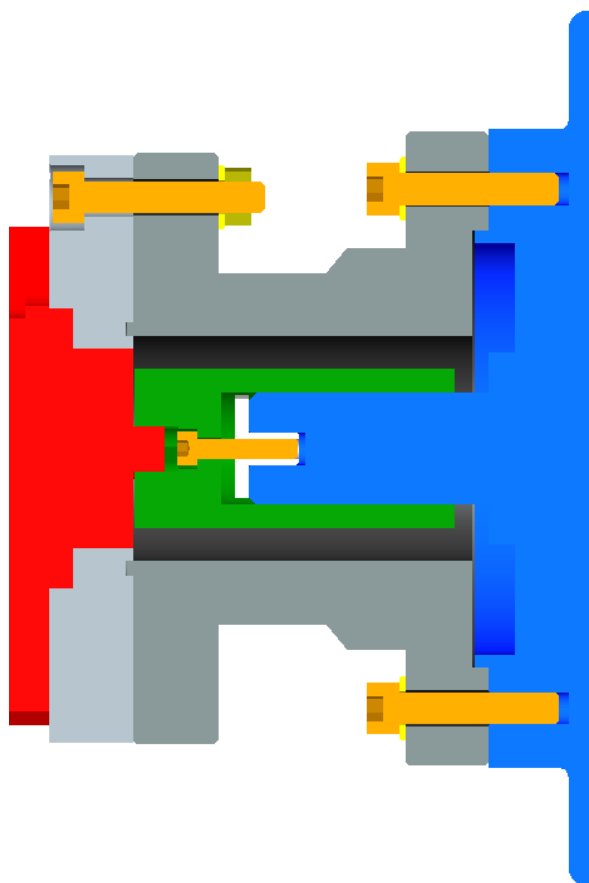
Spojení spojovací hřídele s hřídelí elektromotoru
